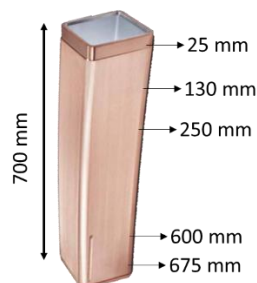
Alturas do molde que foram dimensionadas (Adaptado de KME, 2018)
